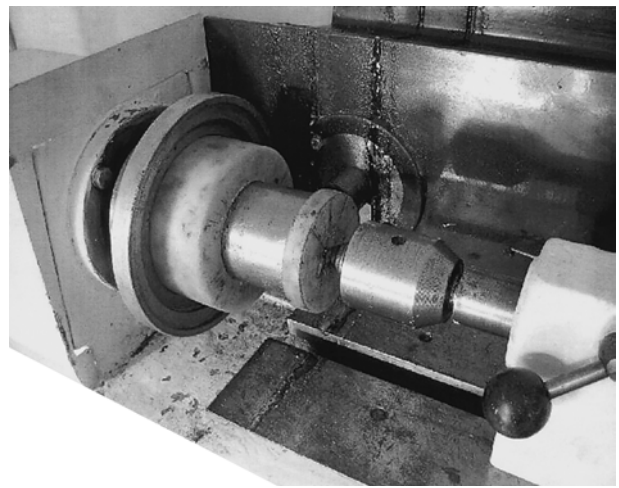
Шпиндельный узел СЦФ-4 с заготовкой
